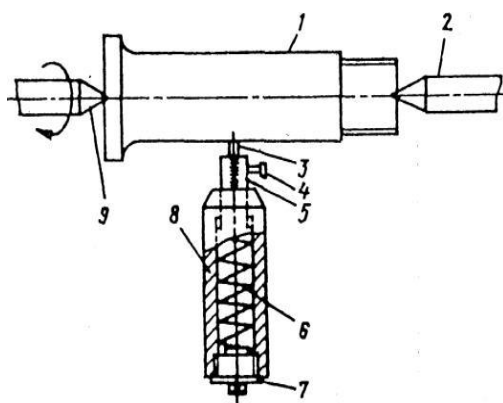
Приспособление для ФАБО валов, болтов и других деталей:
